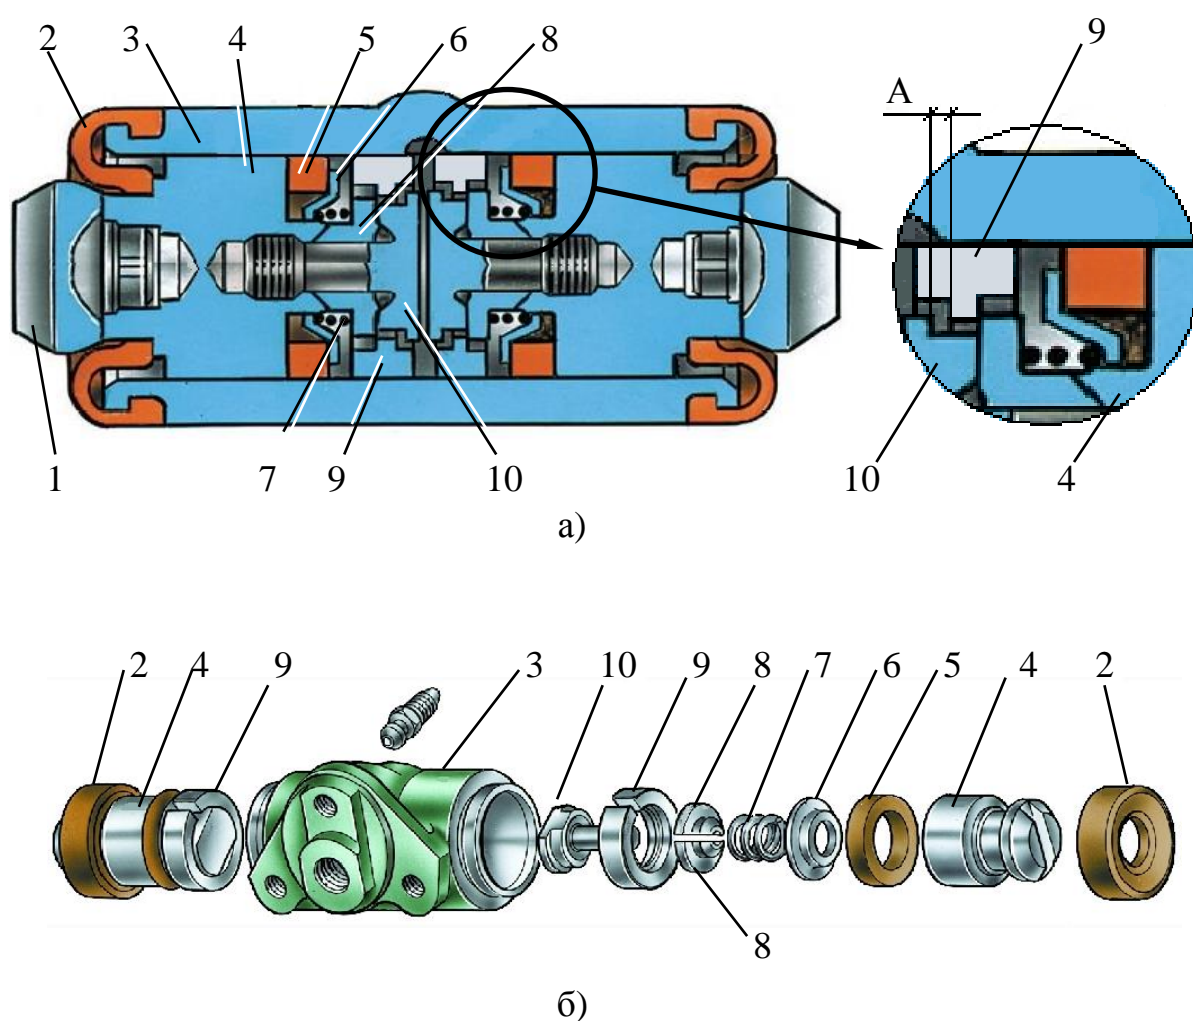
Разрез рабочего тормозного цилиндра с устройством автоматической регулировки зазора между тормозными колодками и барабаном (а), детали и узлы рабочего тормозного цилиндра (б): 1 – упор колодки; 2 – защитный колпачок; 3 – корпус цилиндра; 4 – поршень; 5 – уплотнитель; 6 – опорная тарелка; 7 – пружина; 8 – сухари; 9 – упорное кольцо; 10 – упорный винт; А – зазор
